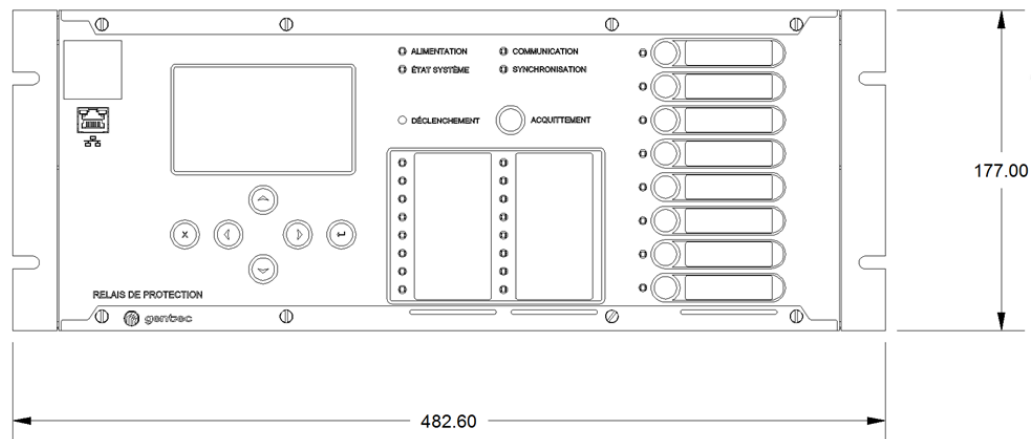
Dimensions physiques - Vue du devant – Famille ALP-4000
